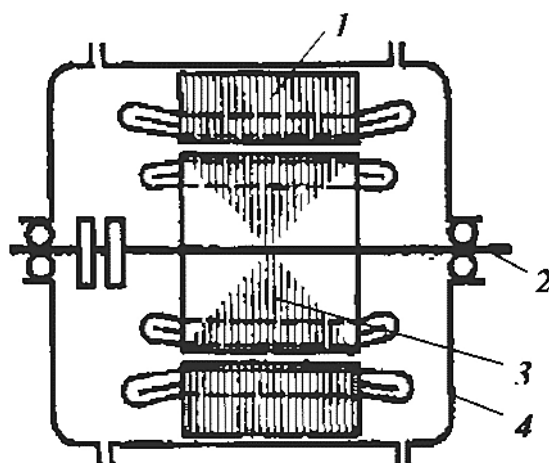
Конструкционная схема вращающегося трансформатора: 1 – обмотки статора; 2 – ротор; 3 – обмотки ротора; 4 – корпус
